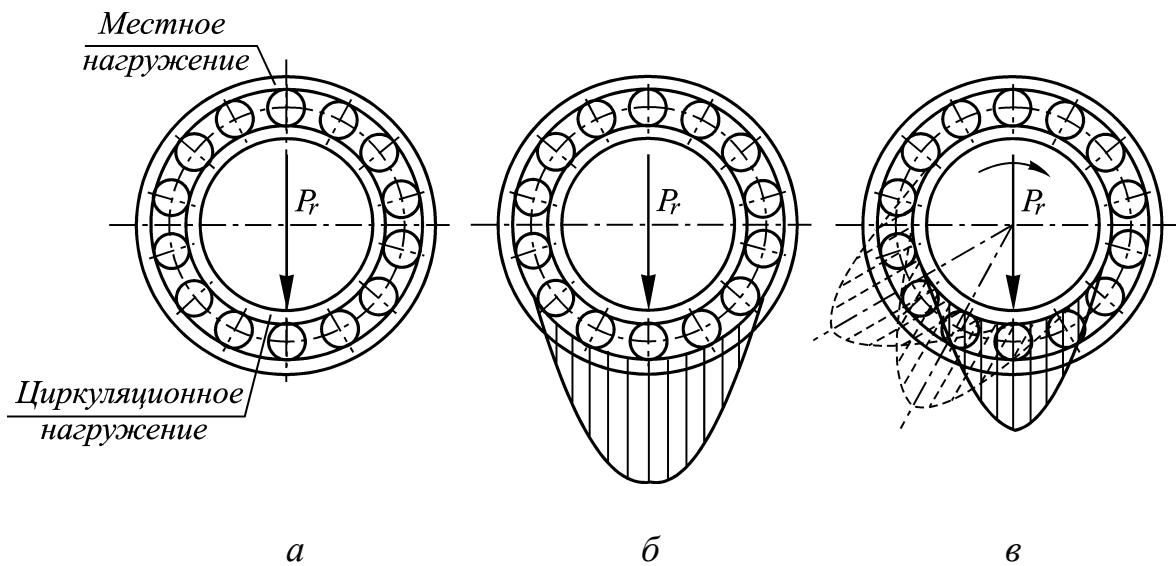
Первая типовая схема нагружения подшипника и виды нагружения колец:
